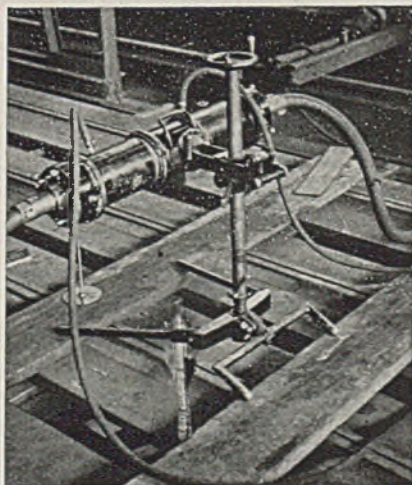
Schweißen der Gurtplattenstöße.
